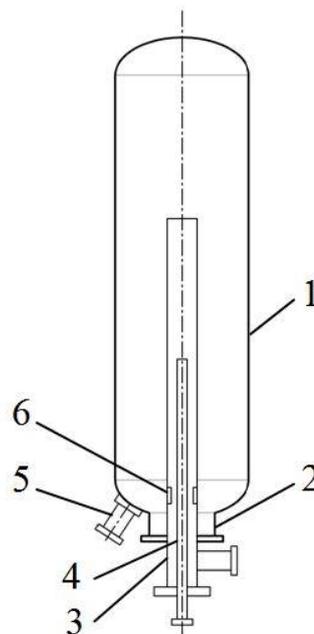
1 – корпус, 2 – горловина, 3 – патрубок загрузки пульпы, 4 – патрубок подачи греющего пара, 5 – патрубок выгрузки пульпы, 6 – отверстия
